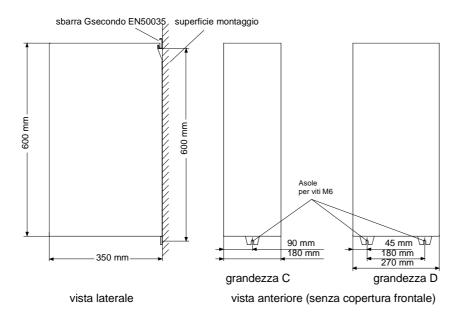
Disegni d'ingombro per montaggio grandezze C, D
